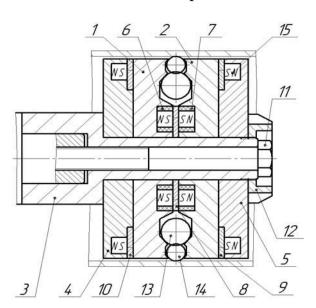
Конструкция магнитно-динамического накатника для модифицирования поверхностного слоя деталей машин и формирования антифрикционных покрытий: 1, 2 — диски; 3 — оправка; 4, 5 — обоймы; 6, 7 — обоймы магнитной системы разгона; 8 — зубчатый магнитопровод магнитной системы разгона; 9, 10 — зубчатые магнитопроводы; 11 — винт; 12 — гайка; 13 — приводные шары; 14 — деформирующие шары; 15 — магниты
